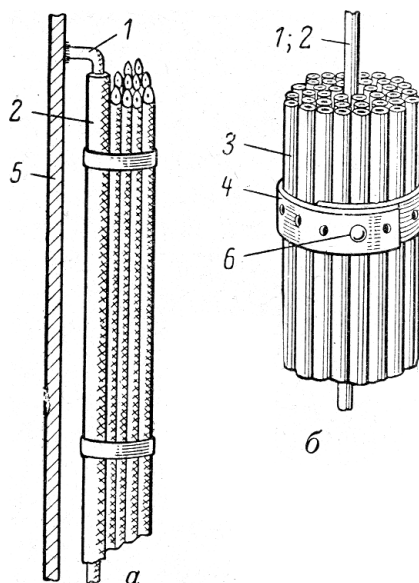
Крепление потока проводов на «струне»: а — одностороннее размещение «струны»; б — центральное размещение «струны»; 1 — «струна» (проволока, прикрепленная к панели); 2 — изоляция «струны» поливинилхлоридной трубкой; 3 — провода потока; 4 — бандаж; 5 — панель; 6 — кнопка для бандажа
